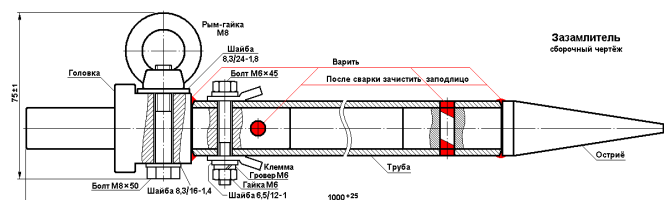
Кол-заземлитель. Сборочный чертёж.
